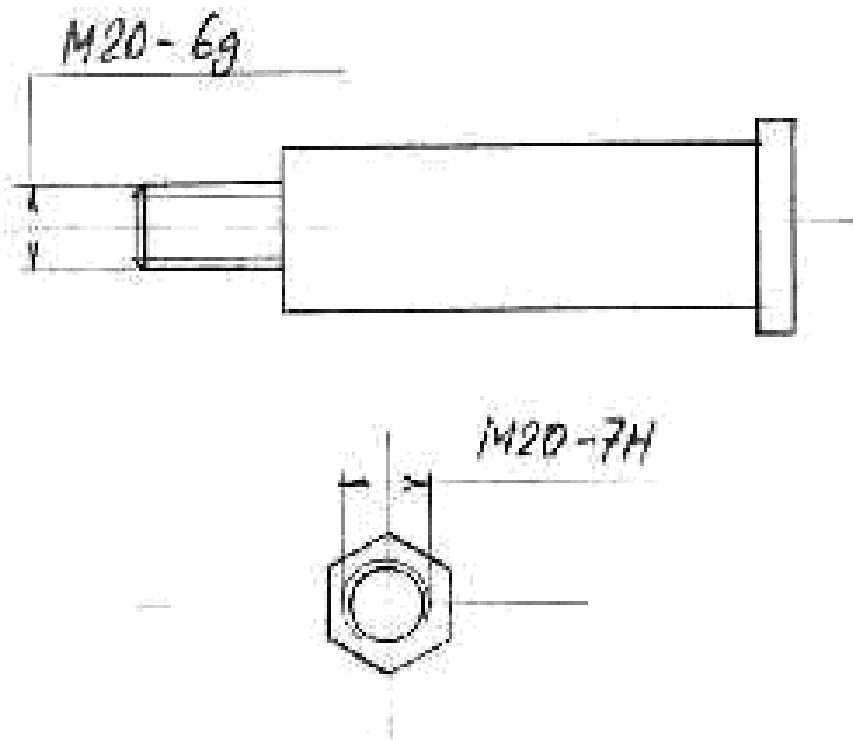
Обозначение метрической резьбы на чертежах деталей
